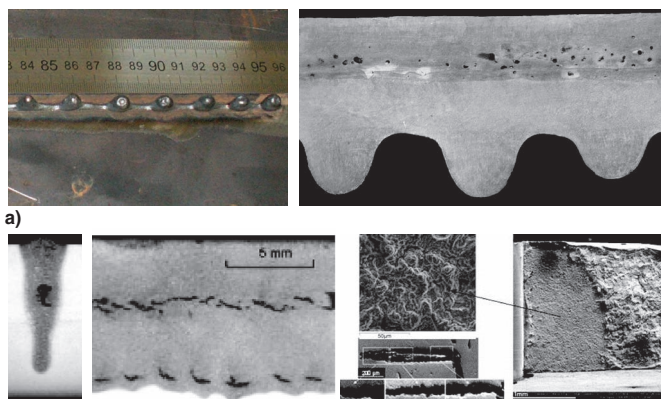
Возможные дефекты при лазерно-дуговой сварке металлов больших толщин: а) нестабильное формирование обратного валика сварного шва (хампинг) и пористость; б) горячие трещины.
